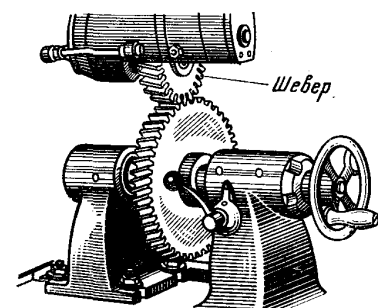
Схема шевінгування зубів круглим шевером
